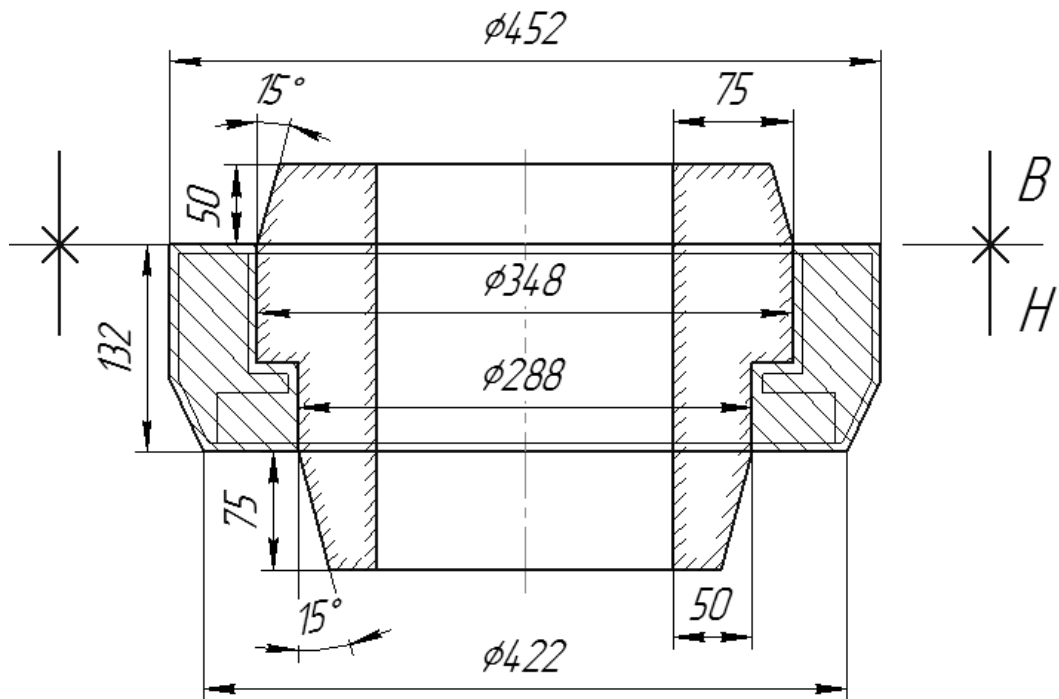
Заготовка деталі "Гайка установочна"
